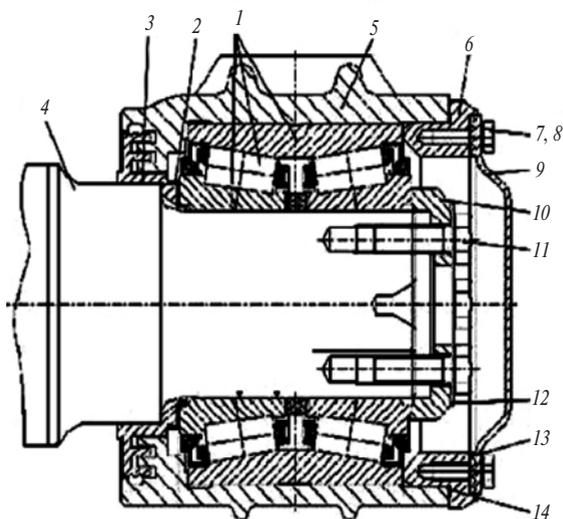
Конструкция буксового узла с подшипниками кассетного типа STBU 130×250×160 (SKF) (правая сторона колесной пары):
